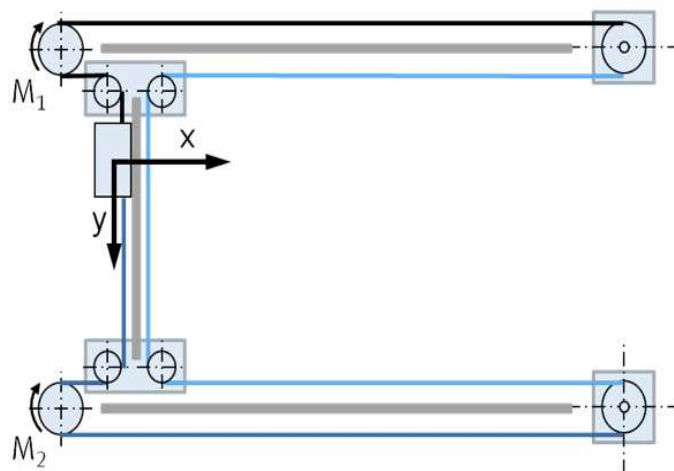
принцип действия Н-портала. M1- двигатель 1, M2- двигатель 2.
